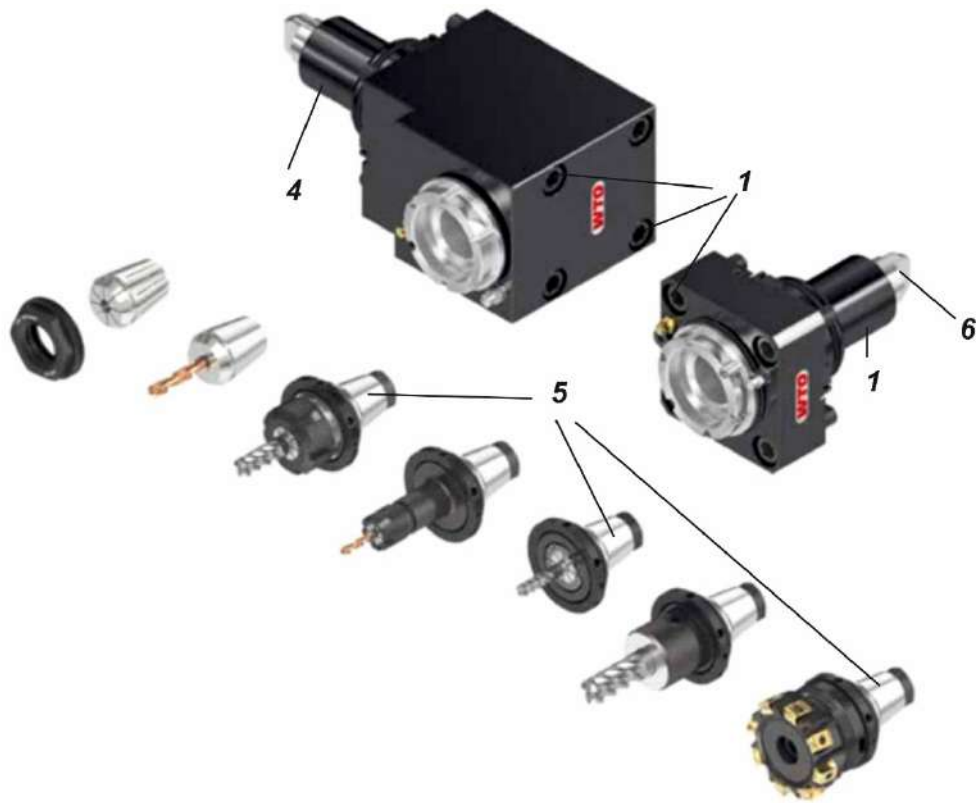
Інструментальна система токарного верстата на основі оправок з конусом 7:24
